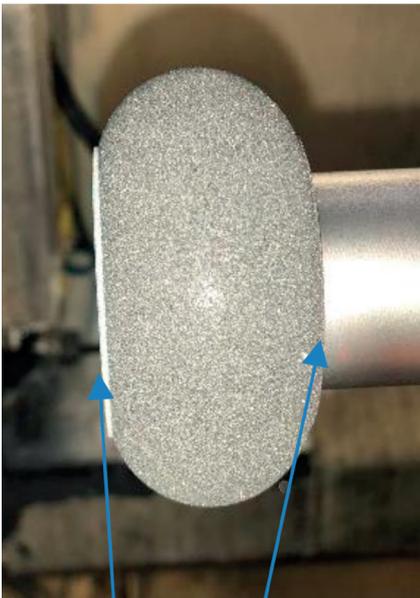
Profilschleifwerkzeug. Die Pfeile zeigen die Umkehrpunkte
